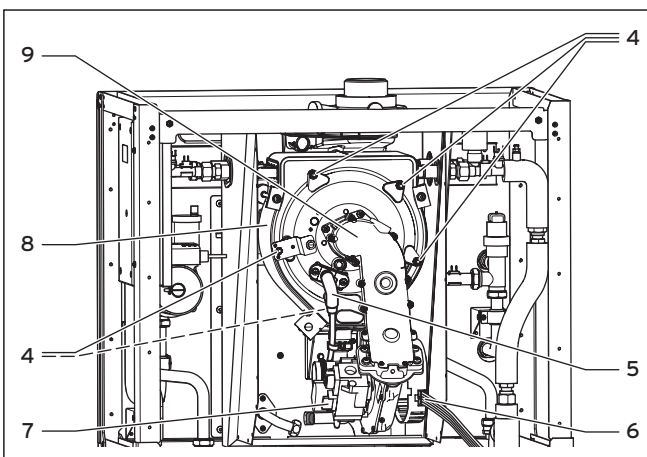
Thermo-Kompaktmodul ausbauen
